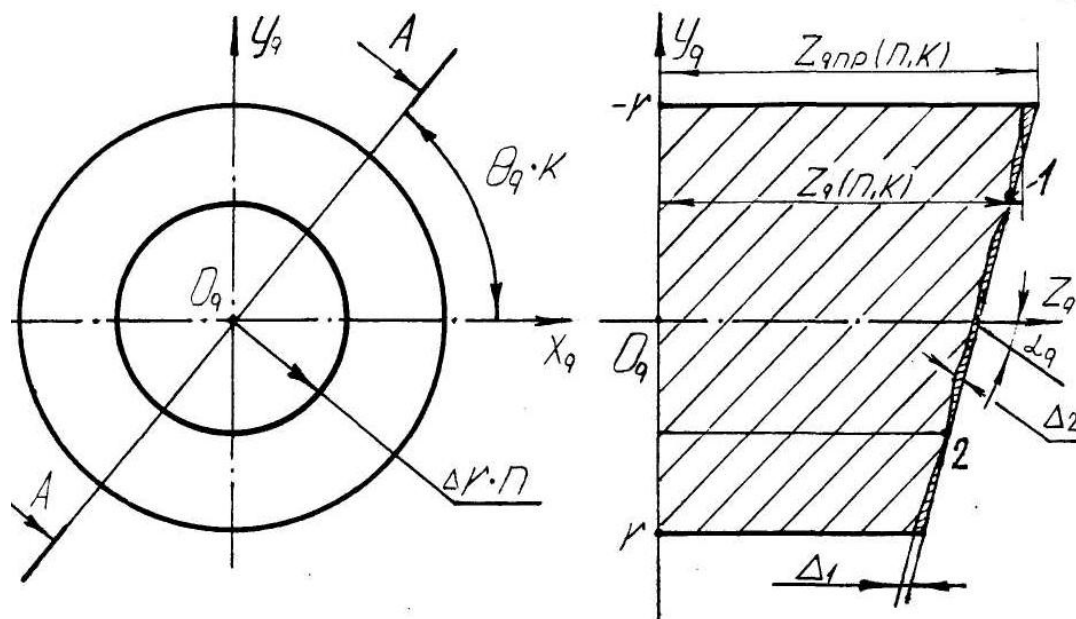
Схема торцевой поверхности цилиндрической детали
